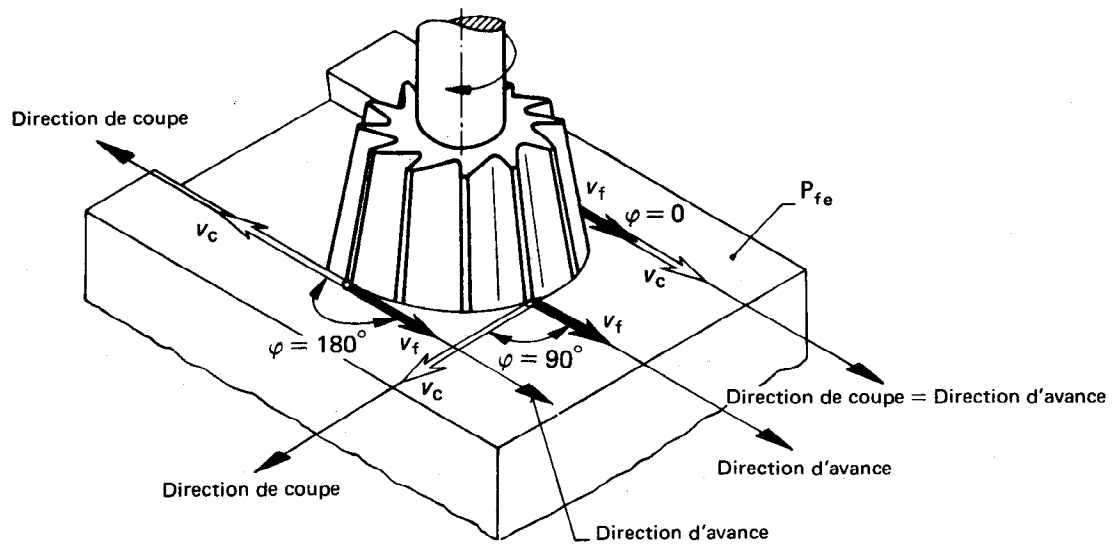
Mouvements de l'outil et de la pièce considérés en trois points choisis sur l'arête – Fraisage conique en bout
